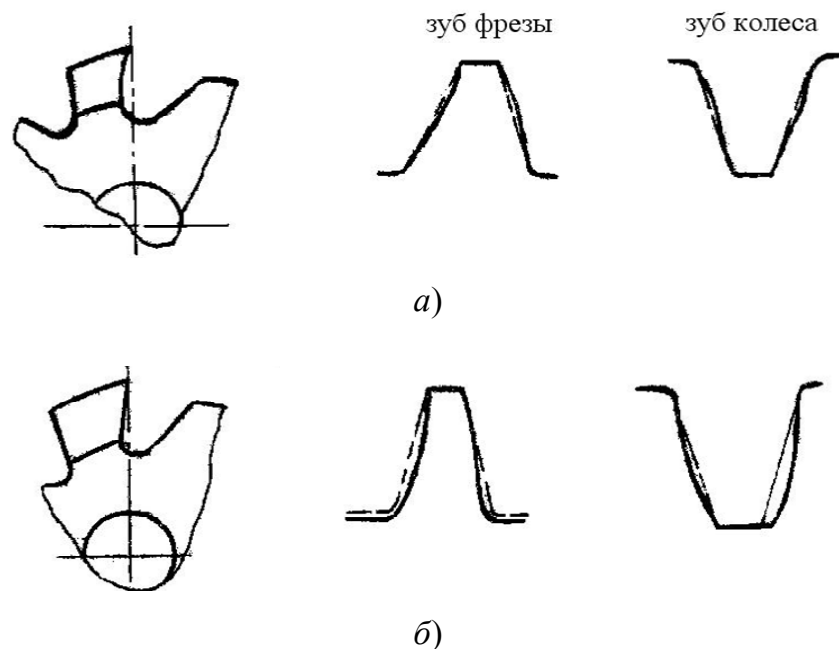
Фрезы передней поверхности зуба фрезы:
